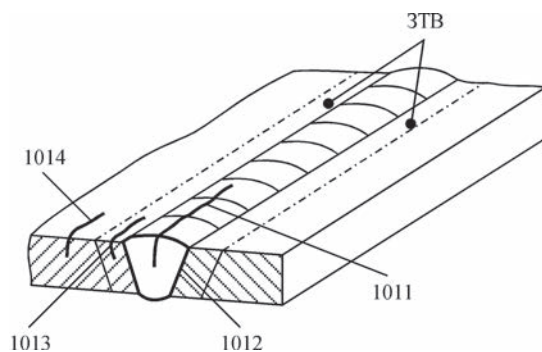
Сварной шов с продольными трещинами: 1011 — в металле шва; 1012 — в зоне сплавления; 1013 — в металле ЗТВ; 1014 — в основном металле [2, 3]
